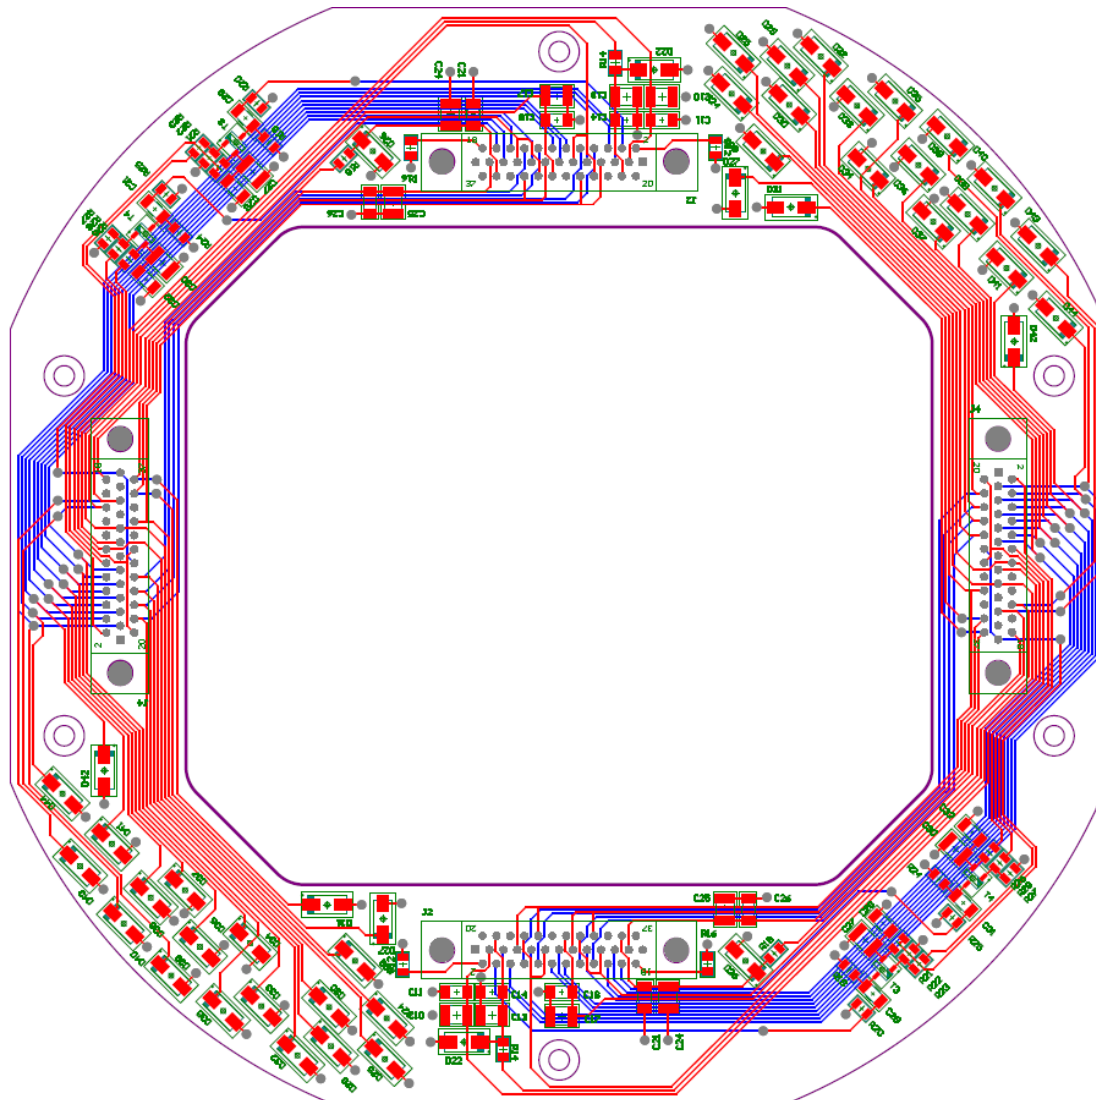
Vue de dessus du PCB (connecteurs “sortent” de la feuille). En rouge, les pistes de la face visible. En bleu, les pistes de la face cachée
